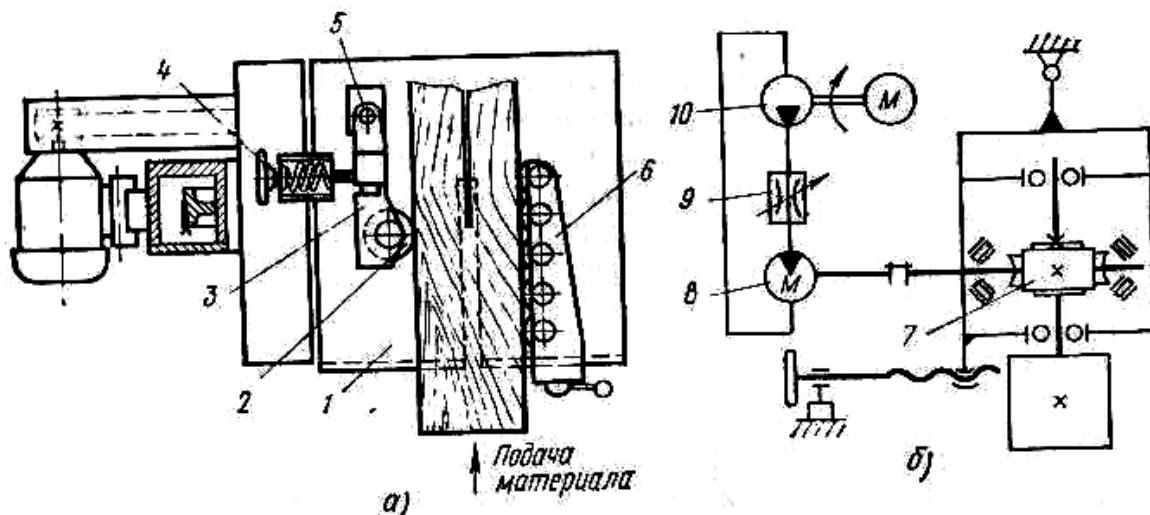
Механизм подачи ленточнопильного столярного станка:
